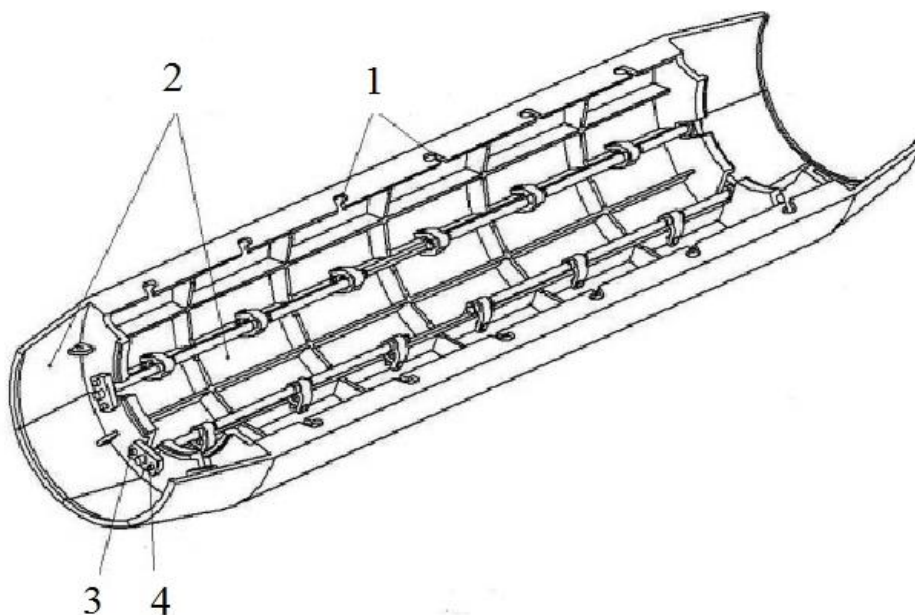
Конструктивная схема металлической разборной оправки с замковым устройством:
